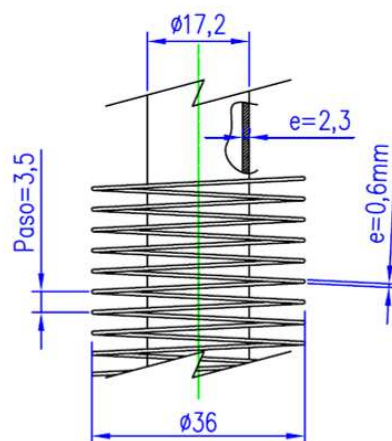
Dimensiones del tubo y aletas circulares del intercambiador de calor.
